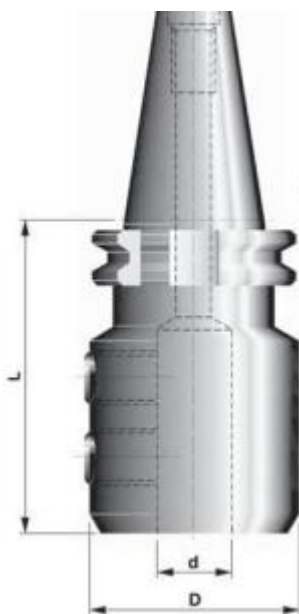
Оправка Weldon SK40×25, L=100 мм
